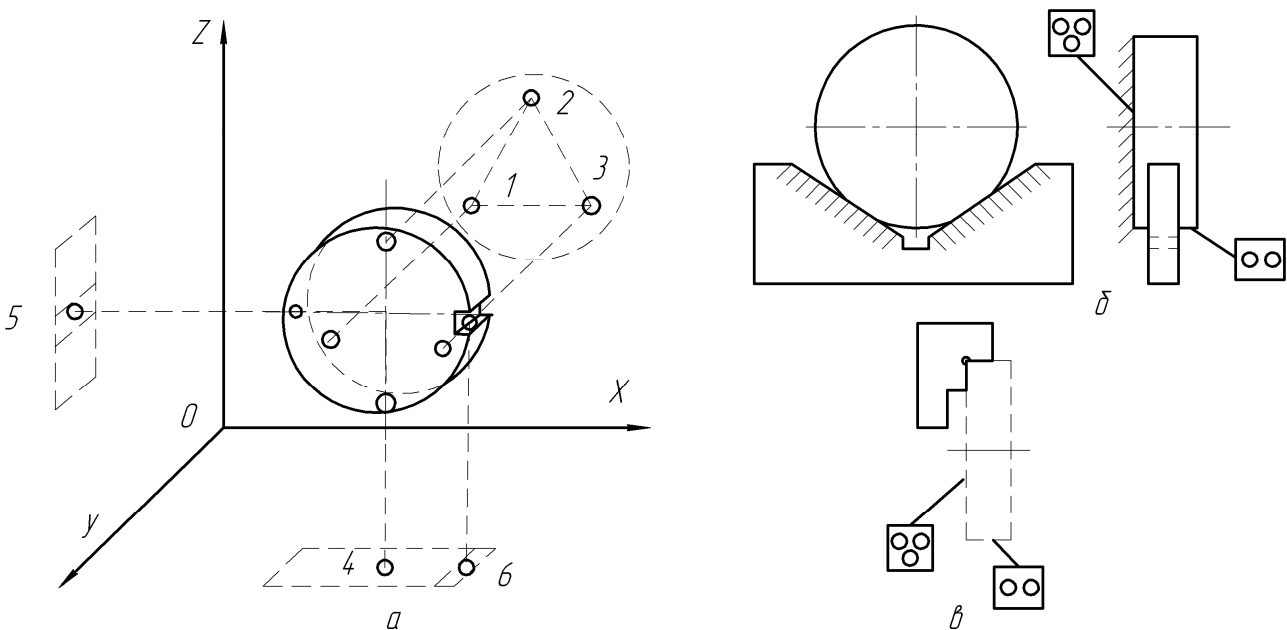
Схема базування коротких циліндричних деталей (диска, кільця)
